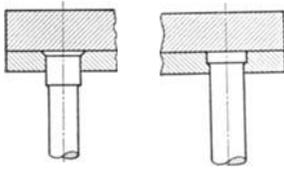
Abb. 117. Abb. 116 u. 117. Bolzenbefestigung in der Kopfplatte durch Preßsitz.
